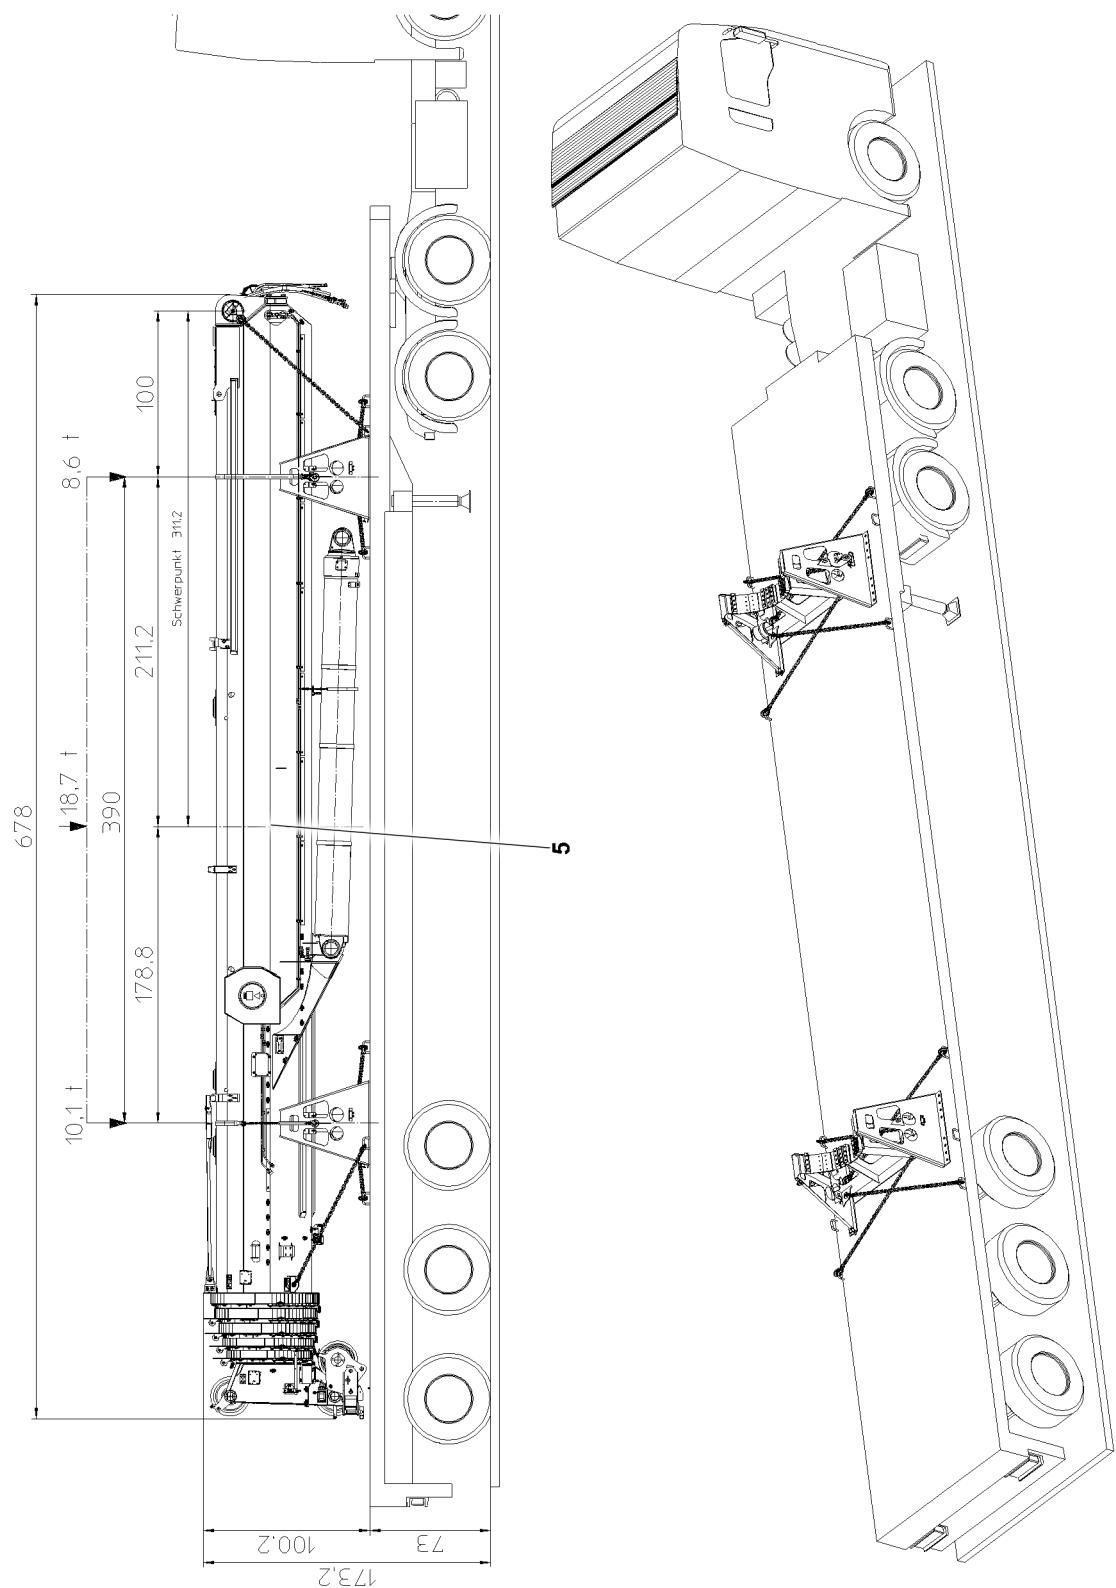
Plan de amarre de los caballetes de transporte con pluma telescópica
